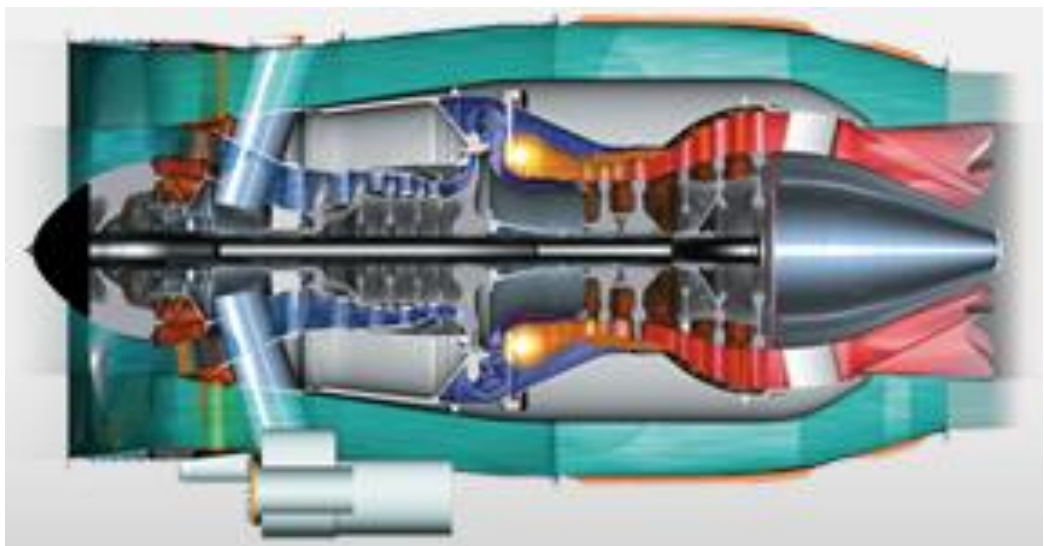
Схематичний загальний вигляд двигуна PW307A
